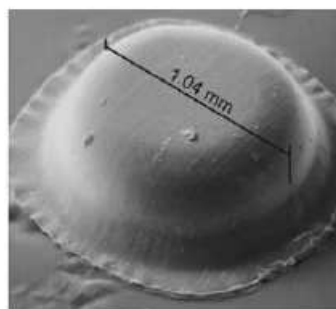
coupelle emboutie (épaisseur du flan = 0,02mm) [VOL04].
